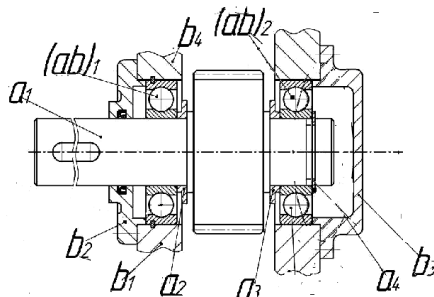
Вал- шестерня с 2-мя подшипниками технологично скорректированная конструкция для автоматического монтажа
